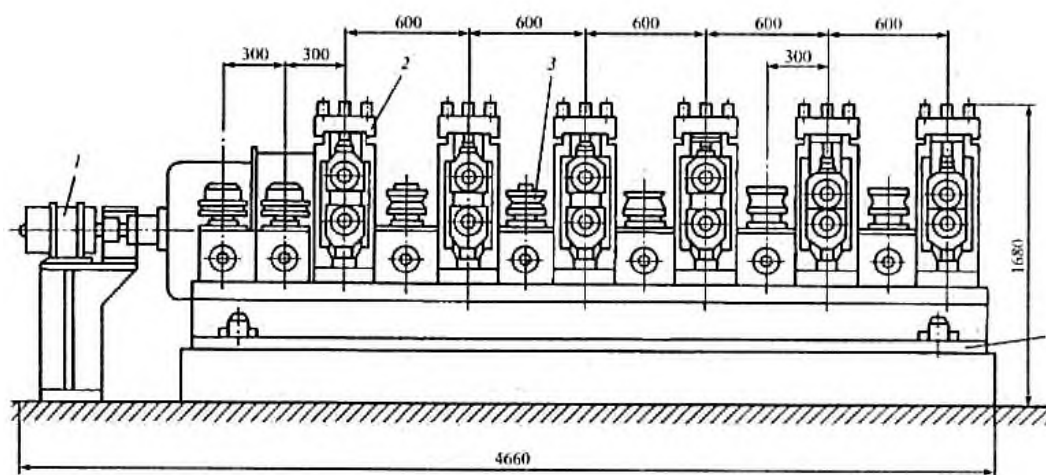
Формовочный стан ТЭСА 20-76 [14]
